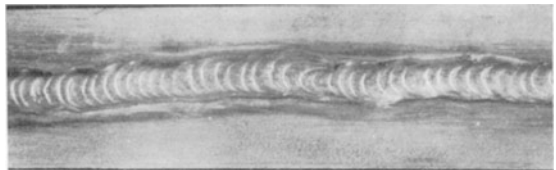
Aluminiumschweißnaht; 3 mm-Blech.
